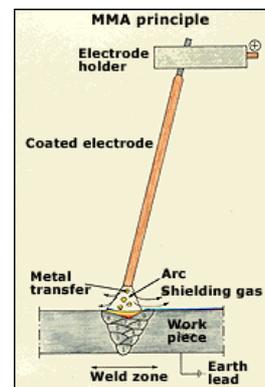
Proceso de Soldadura de Electrodo Cubierto
